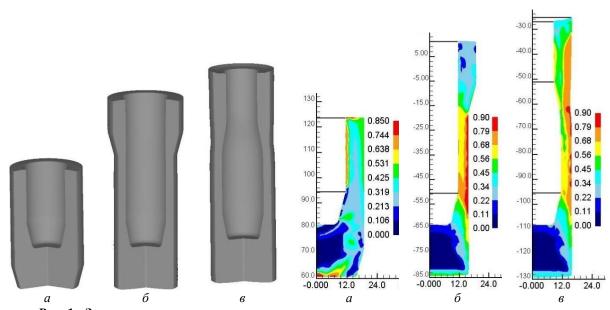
Заготовки после холодного формообразования. Рис. 2 - Распределение
